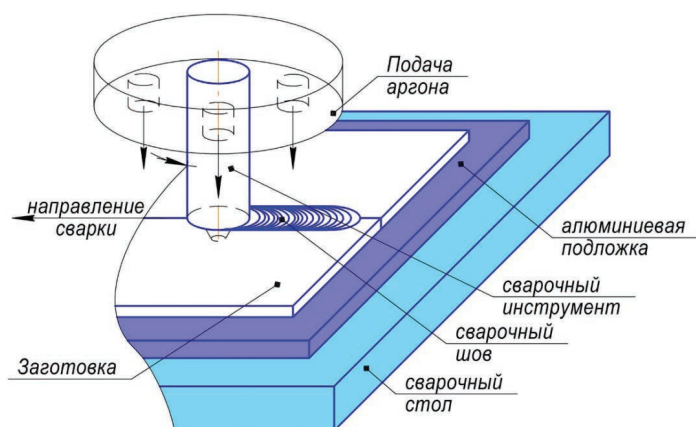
Схема установки сварки трением с перемешиванием титана
